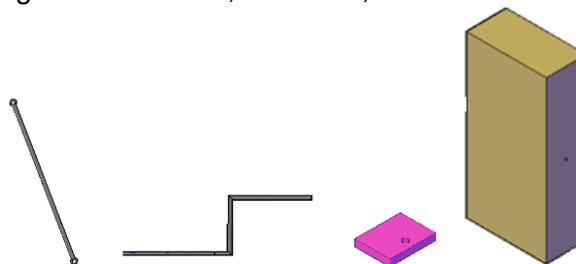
Roberto: trecho retirado do planejamento construído neste LS
